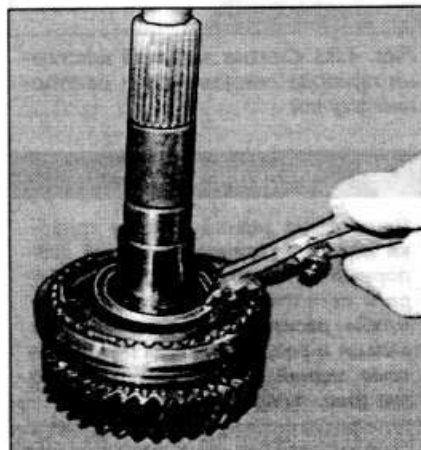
Снятие стопорного кольца ступицы синхронизатора V передачи и заднего хода
